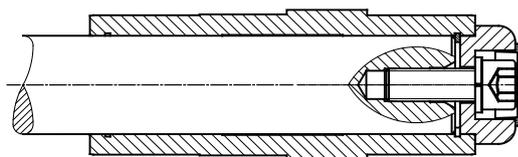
riduttore fissato ad un albero senza spallamento mediante elemento di fissaggio
